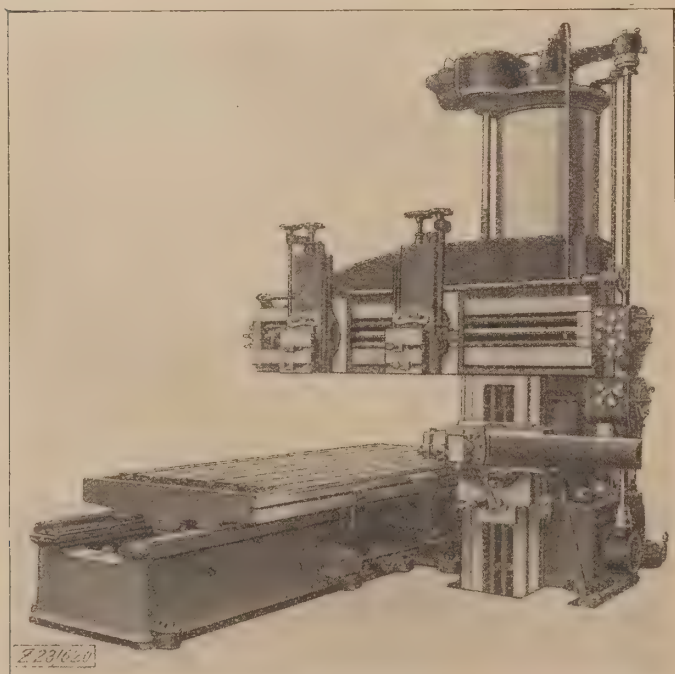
Ein-Säulen-Hobelmachine mit Lauer-Motor von Billeter & Klunz.
